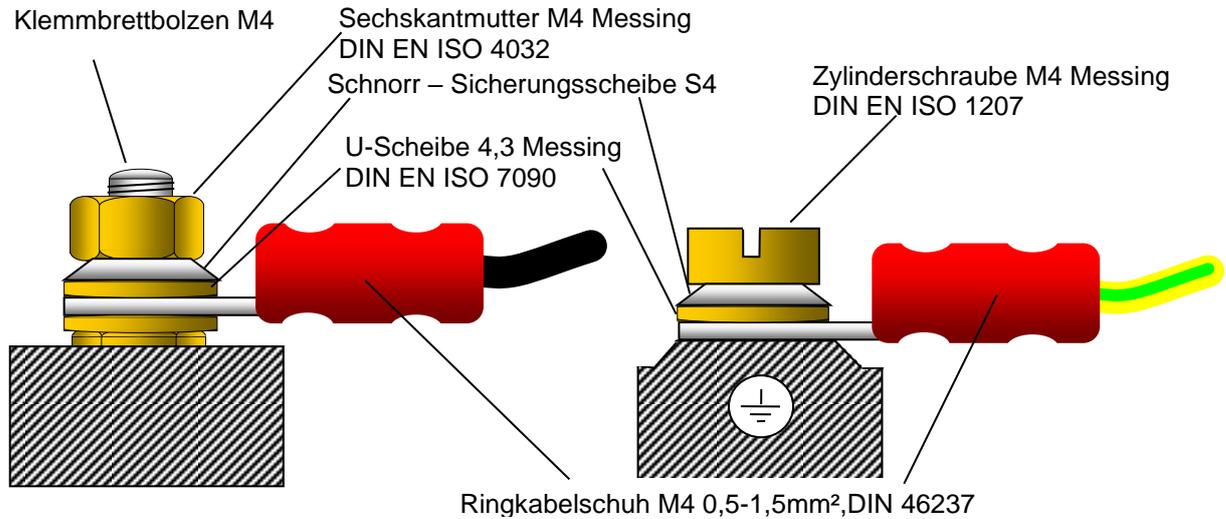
Ausführung der elektrischen Anschlüsse im Klemmkasten
